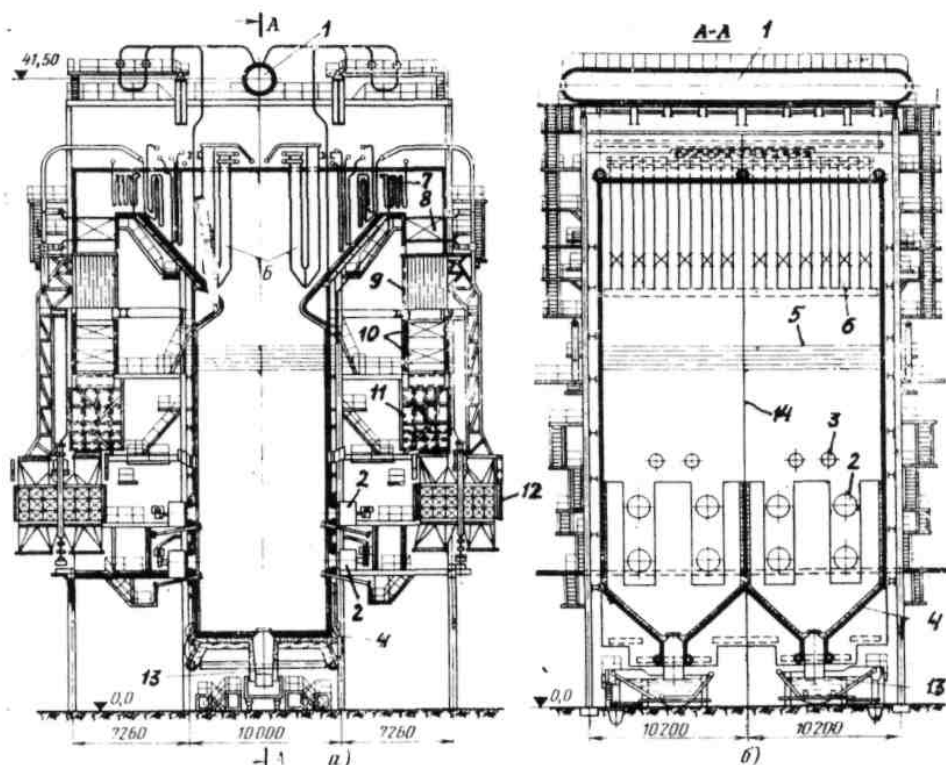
Продольный и поперечный разрез котла ТП-100:
